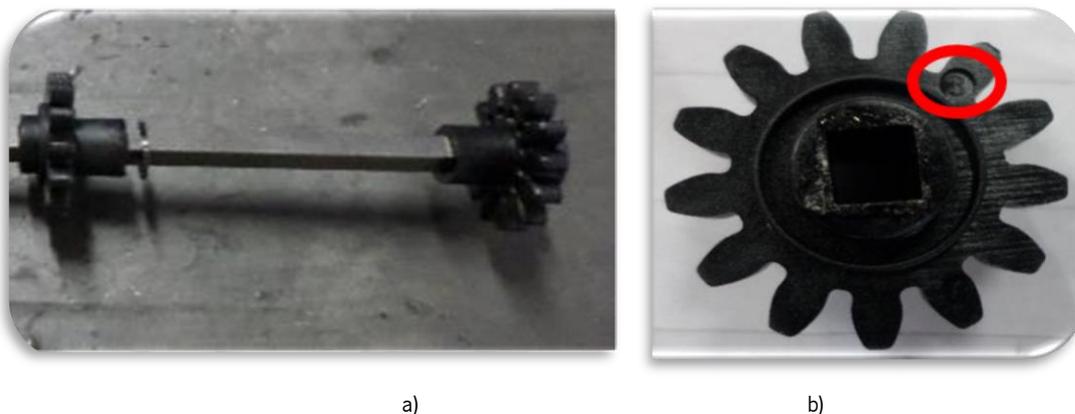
a) Rodas dentadas montadas no eixo; b) símbolo que determina a posição correta
